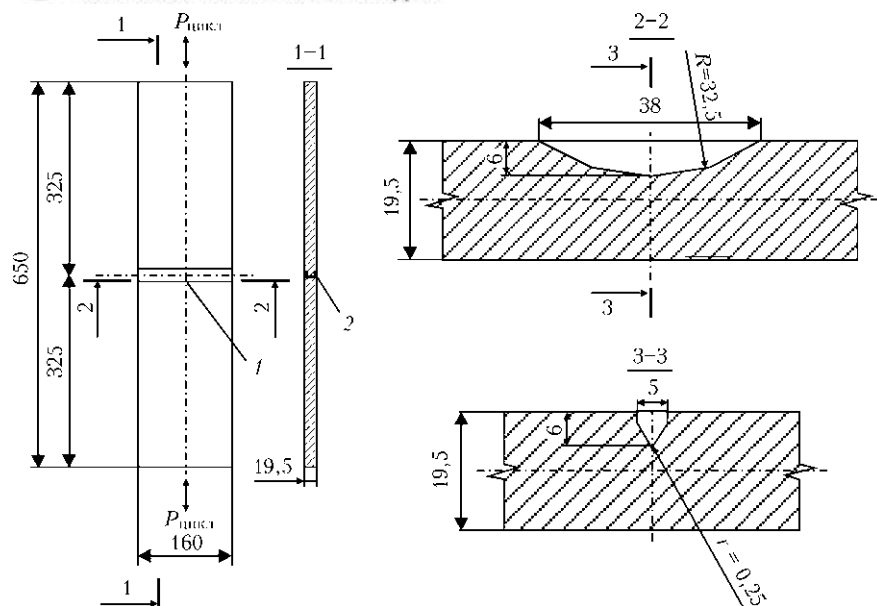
Схема и размеры образцов для испытания сварных соединений стали 06ГБ на циклическую трещиностойкость: 1 — надрез в зоне сплавления; 2 — усиление шва снято с двух сторон
